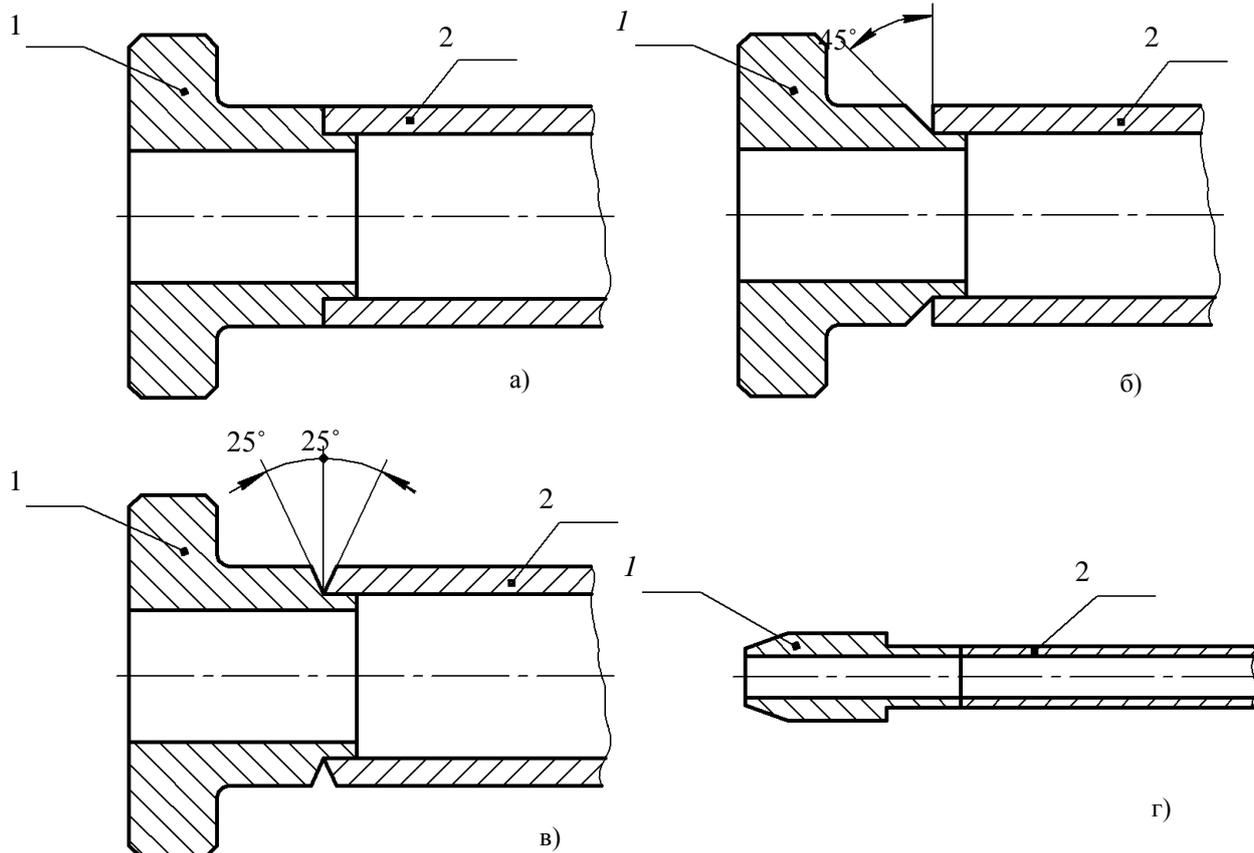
Подготовка кромок разделки под сварку: 1 – фланец (в случае «г»- ниппель); 2 – труба
